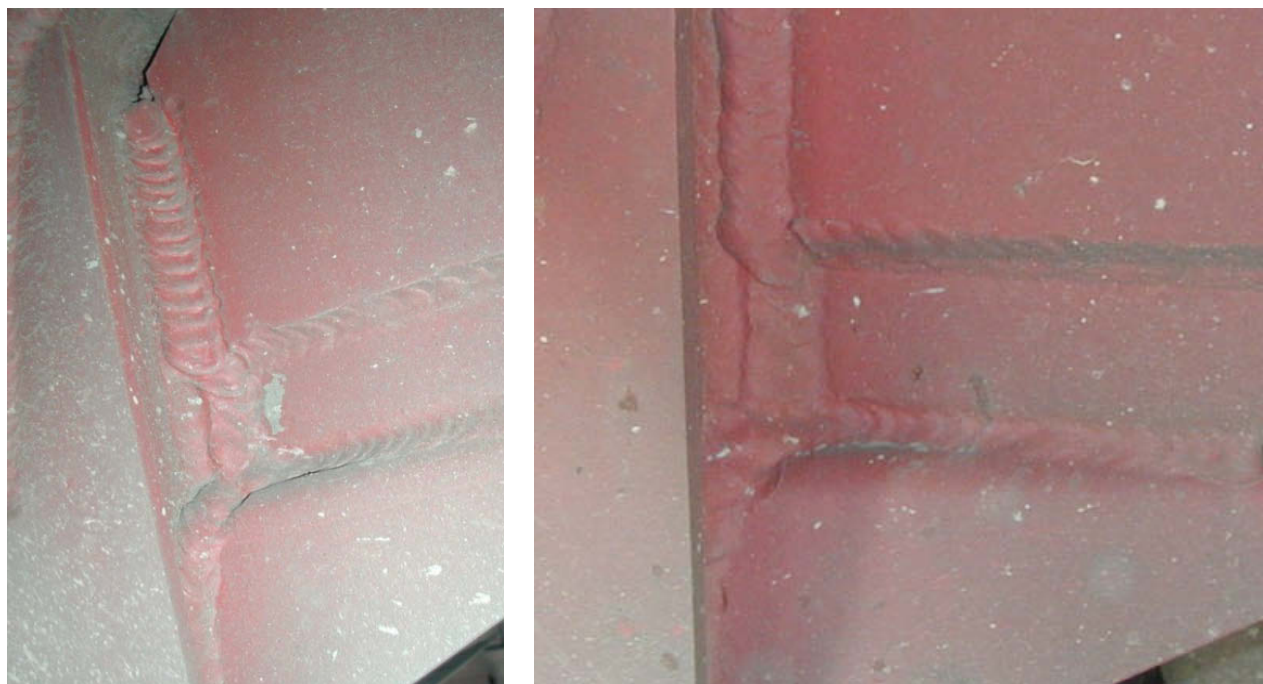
Risse im Auslauf der Schweißnähte der alten Ausführung der Achsanbindung
